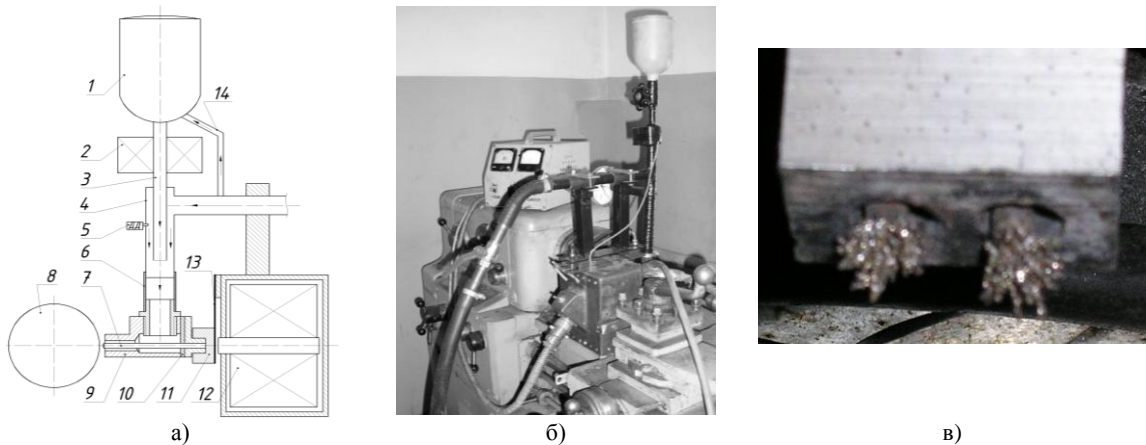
Установка для нанесения ферропорошковых покрытий:
